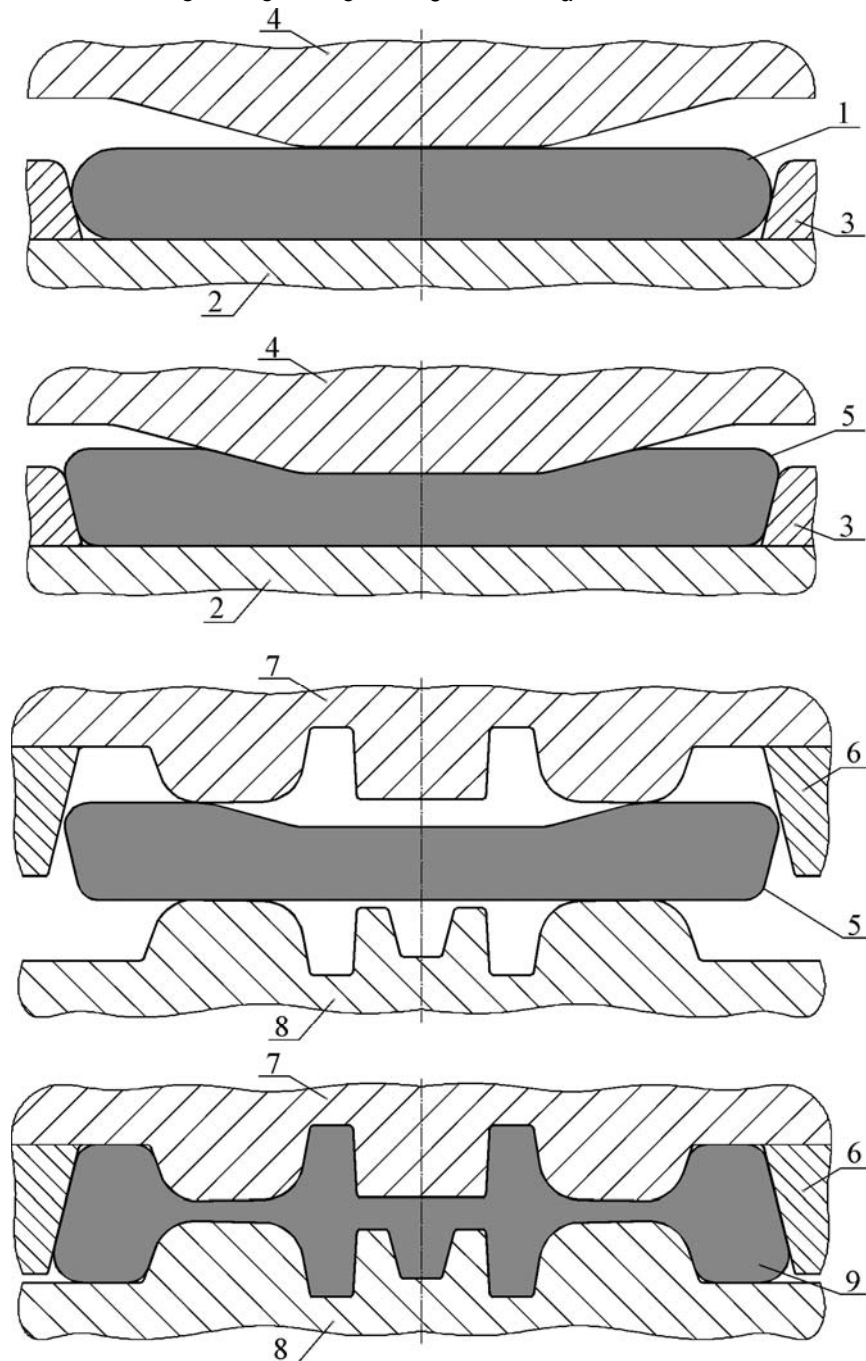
Технологическая схема штамповки колесных заготовок на прессе силой 100 МН из заготовок, полученных разгонкой конусной плитой на прессе силой 50 МН: 1 – заготовка после осадки; 2 – нижняя обжимная плита; 3 – технологическое кольцо; 4 – конусная плита; 5 – заготовка после разгонки; 6 – формовочное кольцо; 7 – верхний формовочный штамп; 8 – нижний формовочный штамп; 9 – отштампованная колесная заготовка с ободом, диском и ступицей
